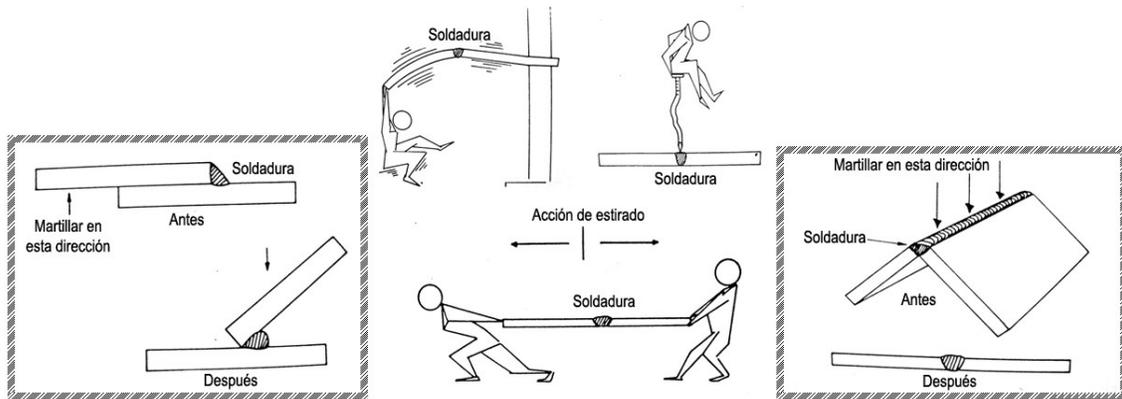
Se muestran las diferentes pruebas destructivas que pueden llevarse a cabo para saber si se realizó una buena aplicación en la soldadura. De izquierda a derecha tenemos en primer lugar una prueba en la que se martilla hasta lograr un doblado de 180 grados, en la figura central se presenta una prueba de flexión y tracción, por último a una unión en "V" se le martilla hasta dejarla en un plano horizontal.
